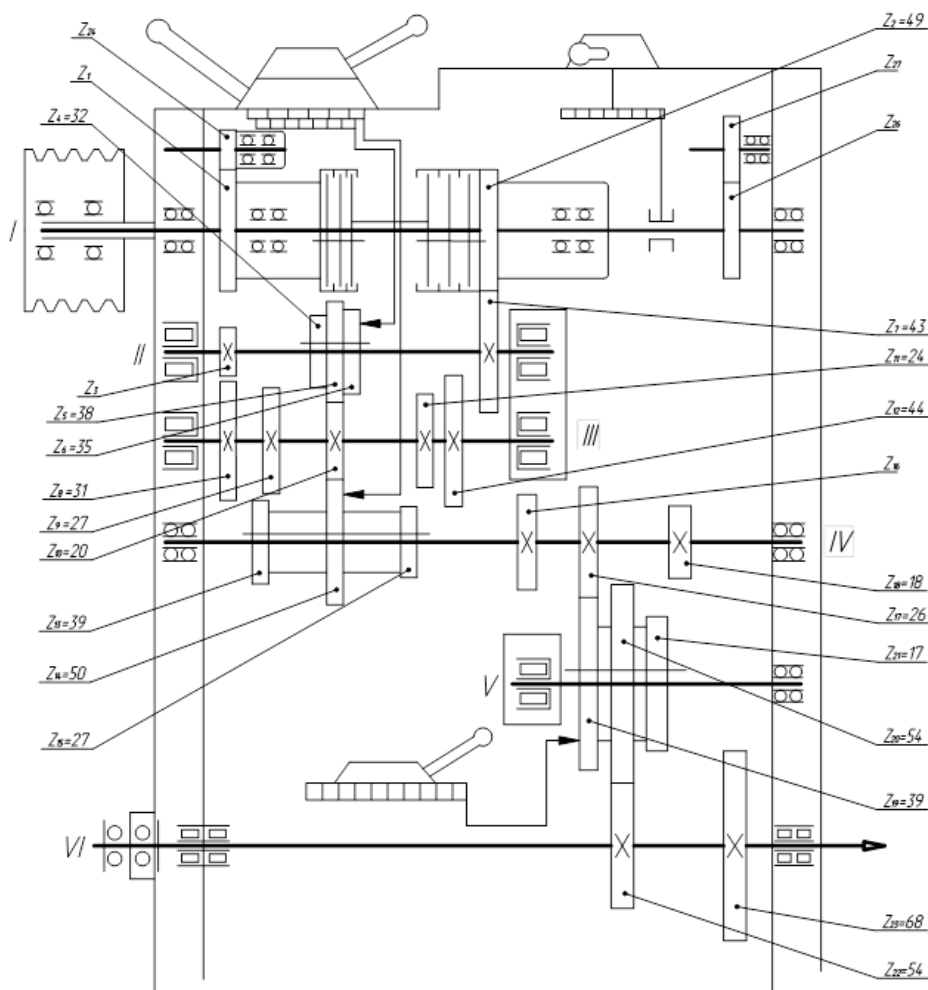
Кинематическая схема коробки передач универсального токарного станка СН-401/501
